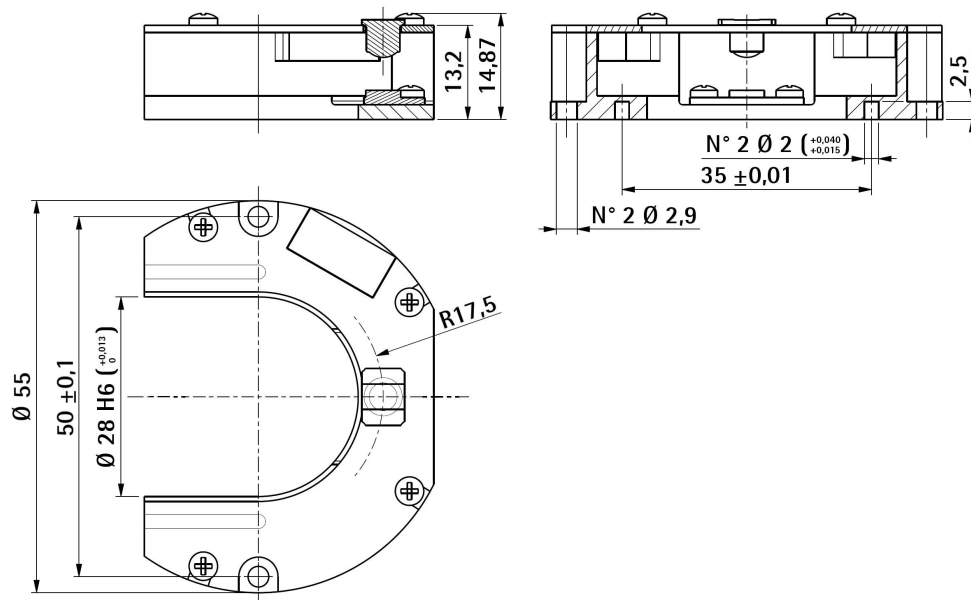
Dimensioni di ingombro dell'encoder AMM5A
